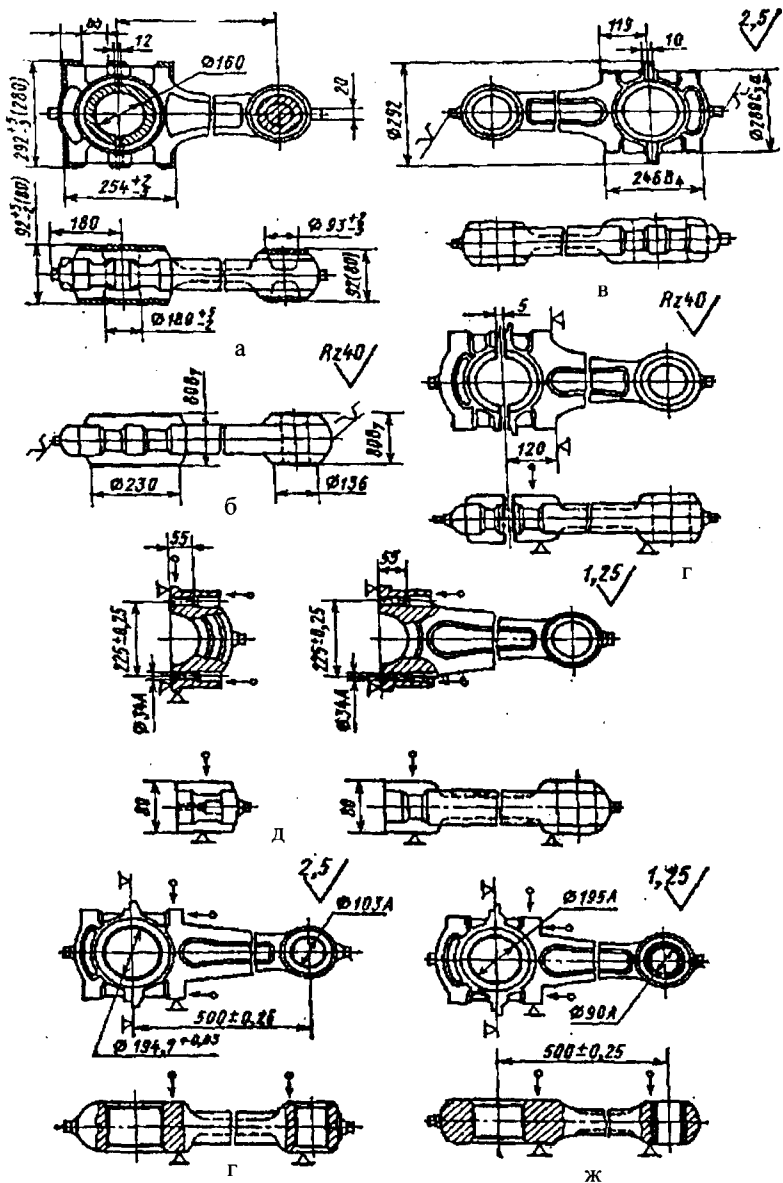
Технологічна схема механічної обробки шатуну опозитного компресора бази М10.
